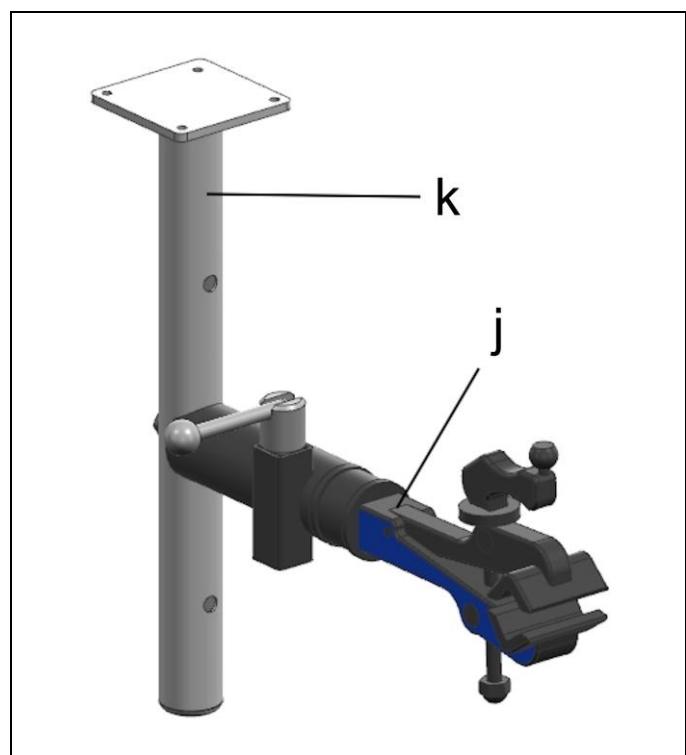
Clamping Claw „Park Tool“ with Adapter
